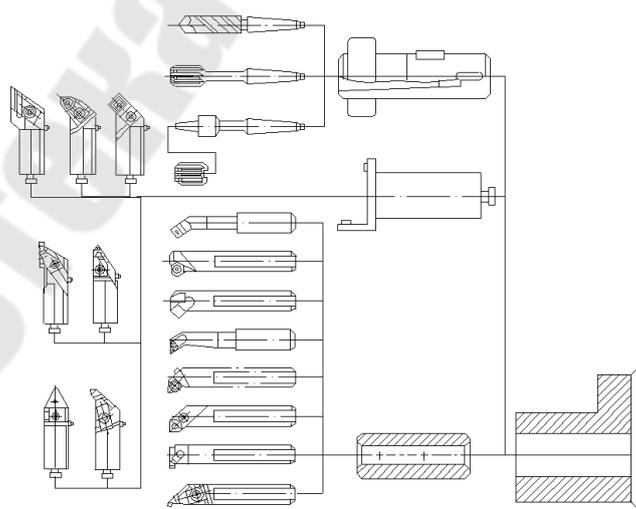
Комплект режущего инструмента для токарного станка с УЧПУ модели 16К20Ф3
